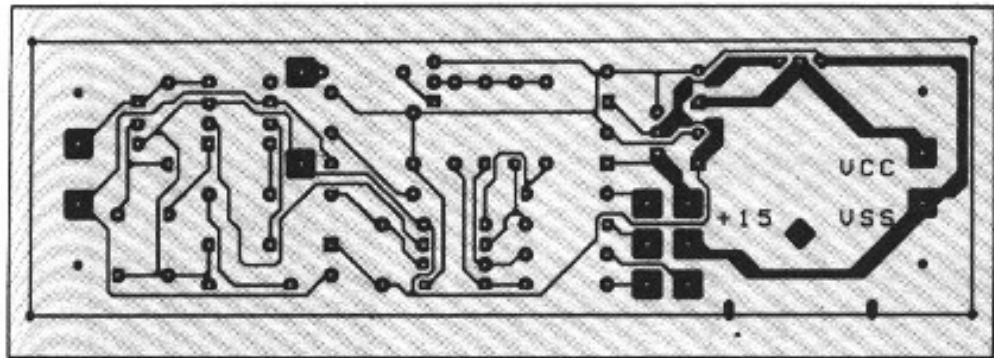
Circuit imprimé du module récepteur de la télécommande, côté soudures.
